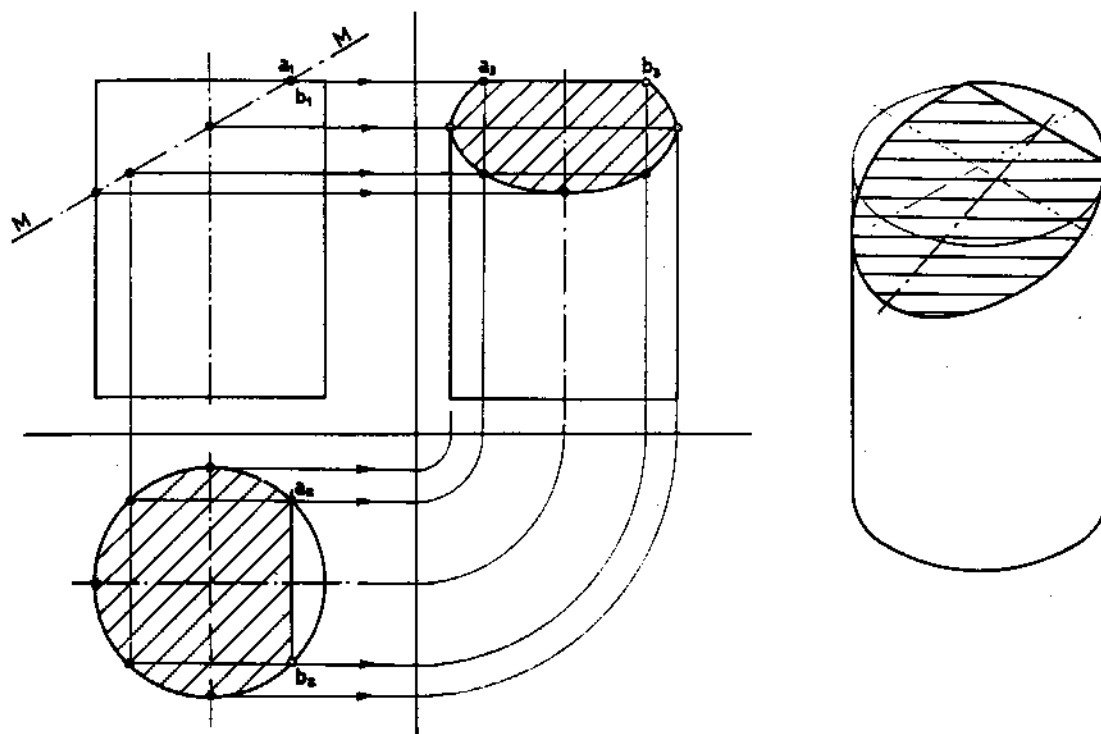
Sezione parziale di un cilindro con un piano di traccia MM ortogonale al P.V., inclinato sul P.O. e avente la posizione indicata. La sezione sul P.L. risulta un segmento di ellisse.
